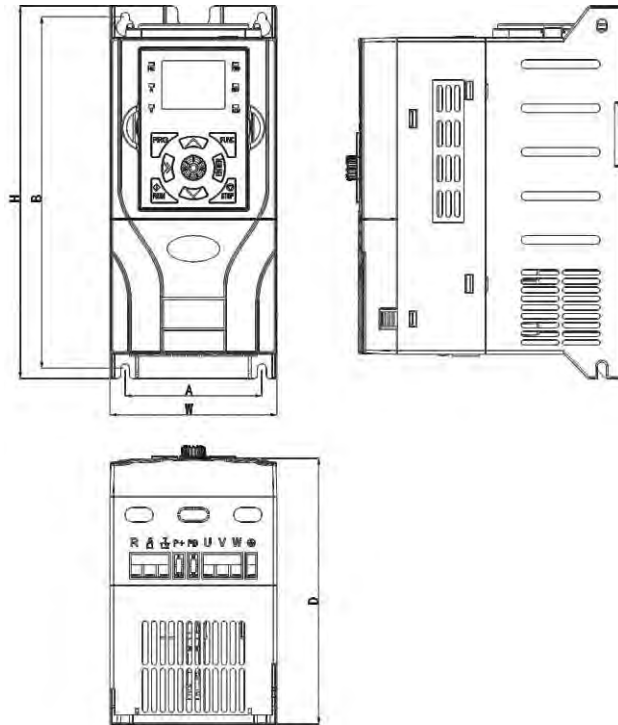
Dimensiones del inversor 0,75KW ~ 30KW
